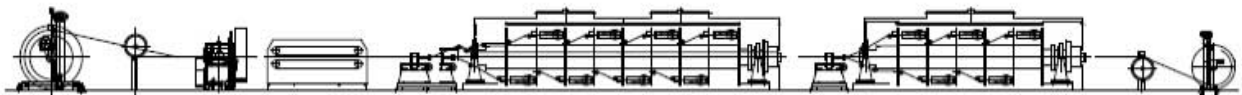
Схема сталедрутової канатної машини сигарного типу Sket SRN 6x800
